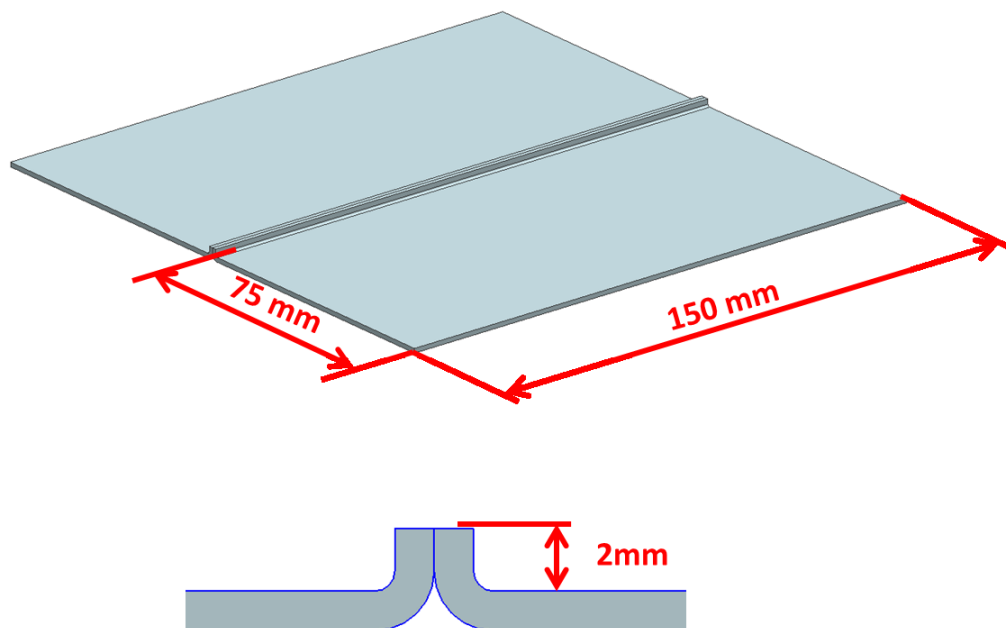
Corpo de prova para soldagem GMAW (Próprio autor).
